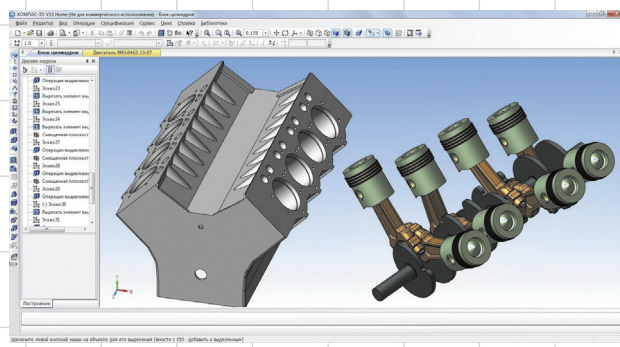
Блок цилиндров и кривошипно-шатунный механизм
